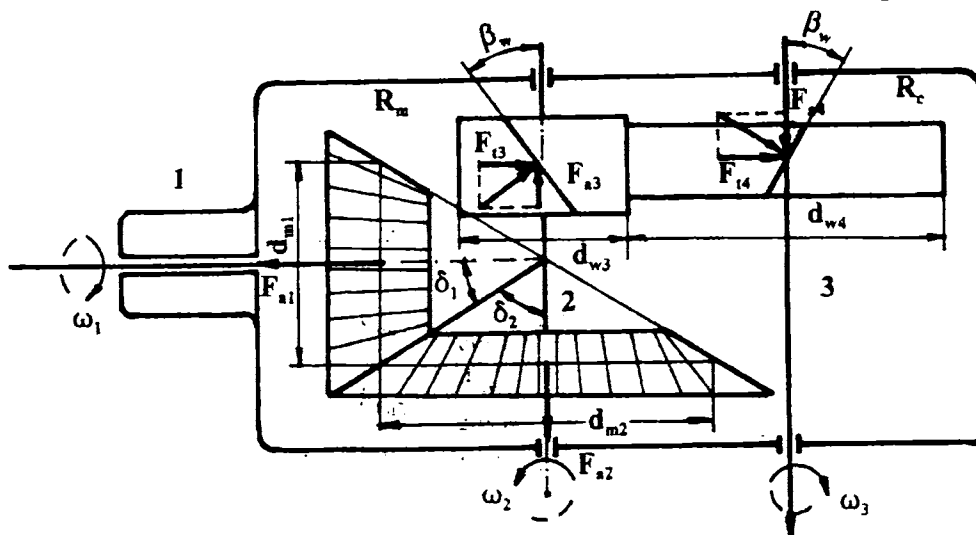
Sensurile forțelor axiale într-un reductor conico-cilindric.
